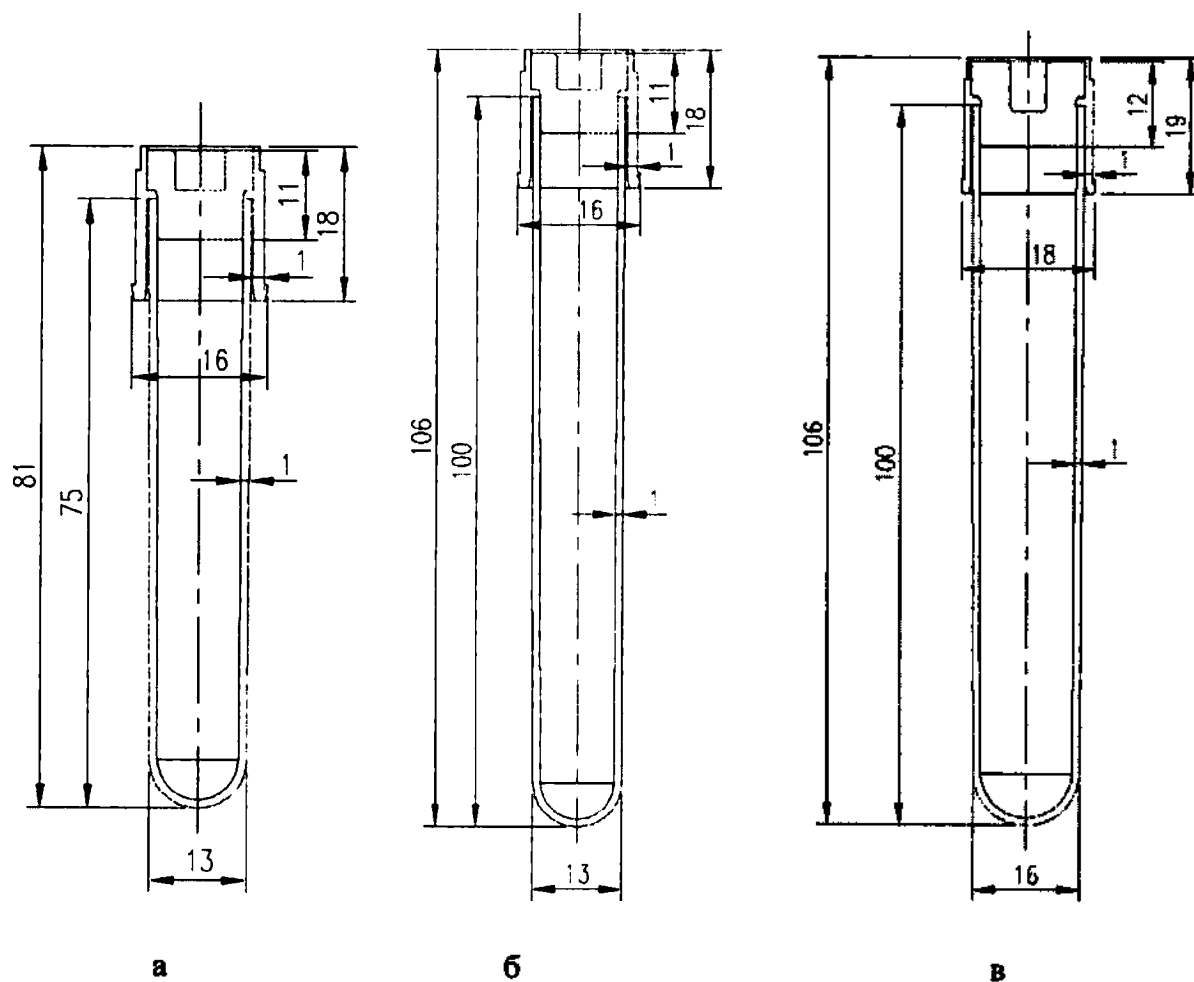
Сборочный чертеж пробирки вакуумной для взятия венозной крови, где:
